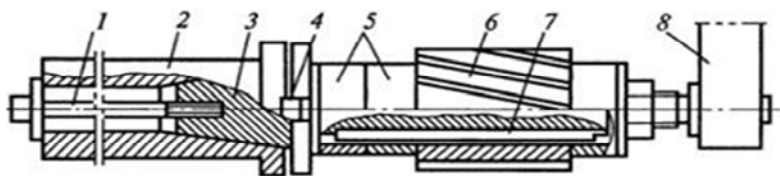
Установка цилиндрической фрезы на центральной оправке:
